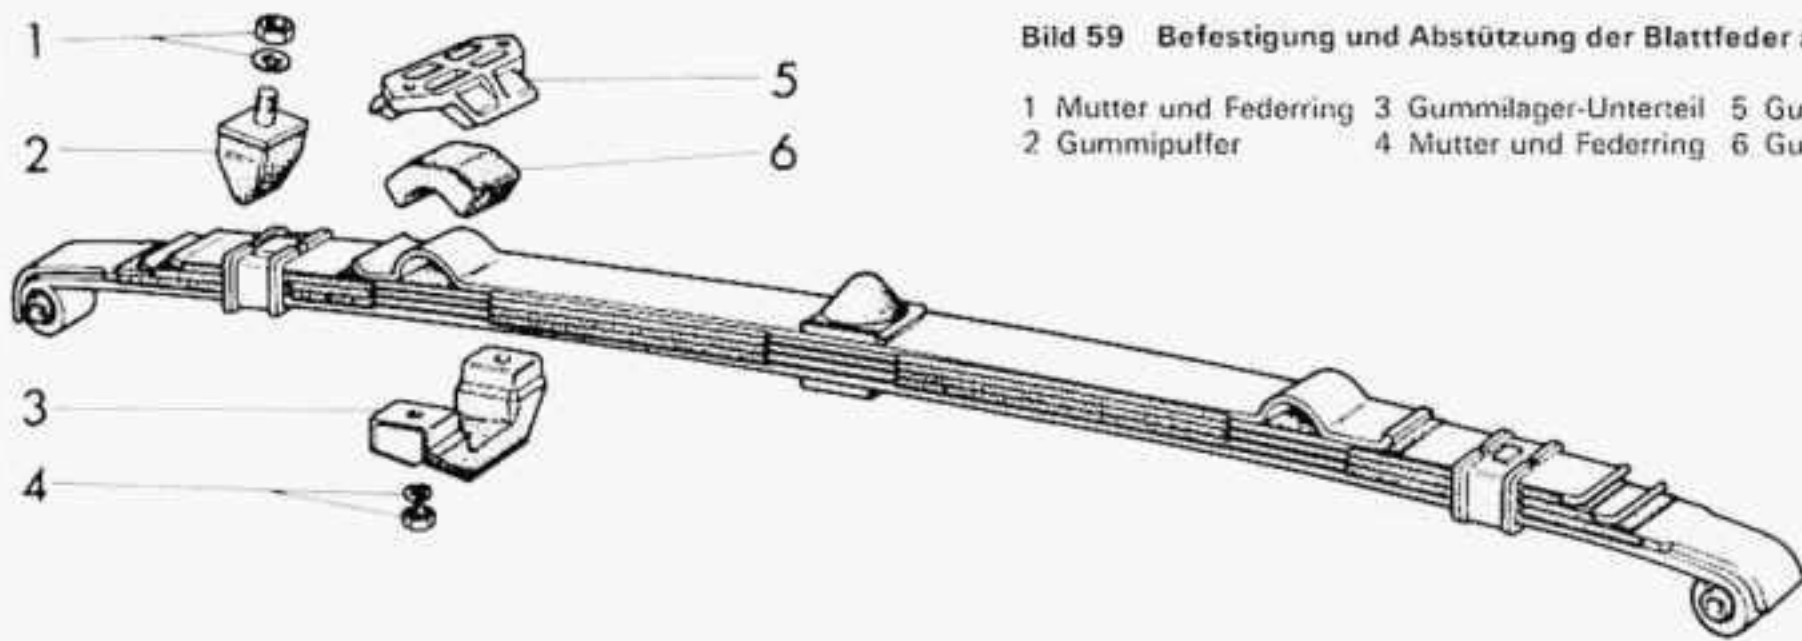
Befestigung und Abstützung der Blattfeder an der Karosserie
